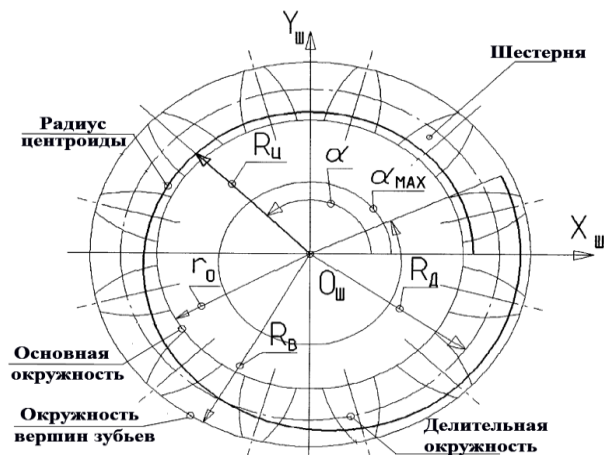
Шестерня с переменным радиусом центроиды [5]
